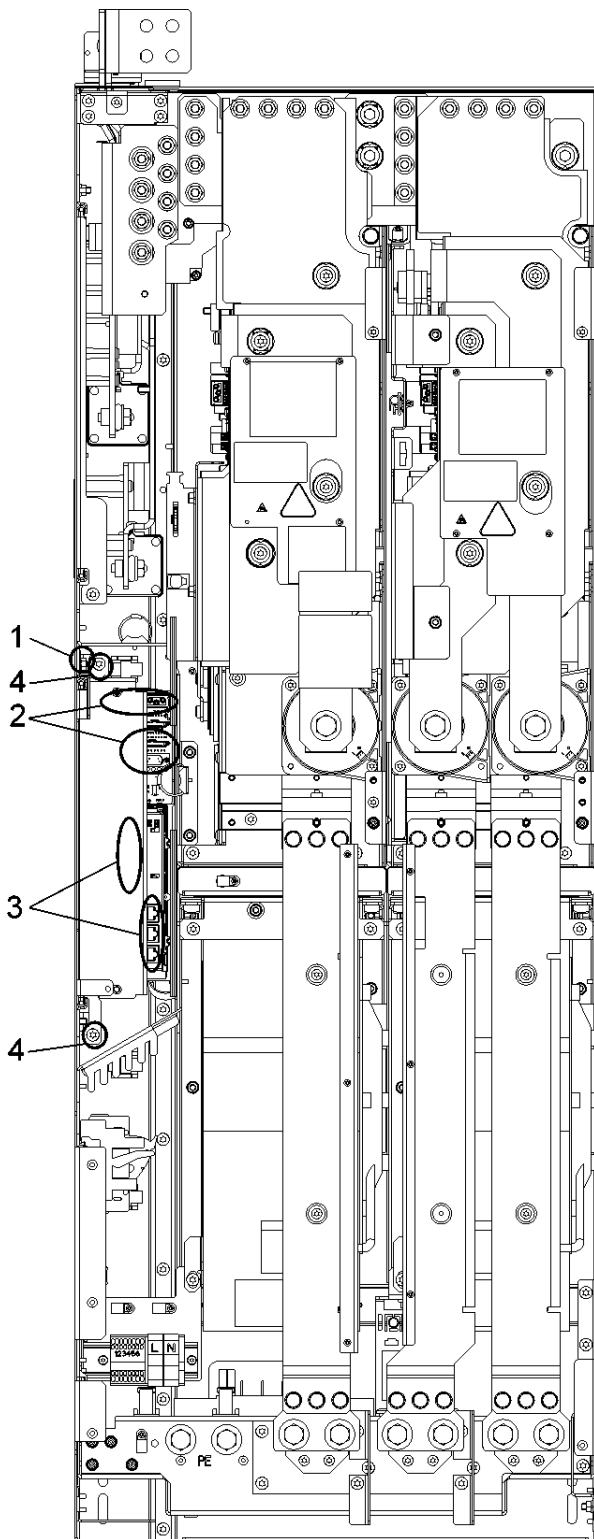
Austausch Control Interface Board, Baugröße HX
